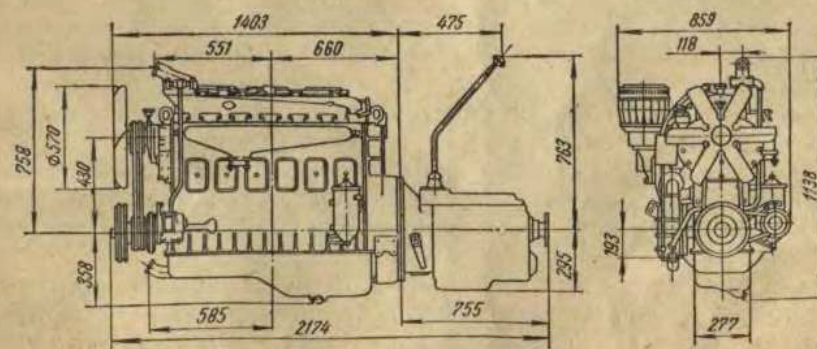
Габаритные размеры двигателей ЯАЗ-М206Б и ЯАЗ-206К
